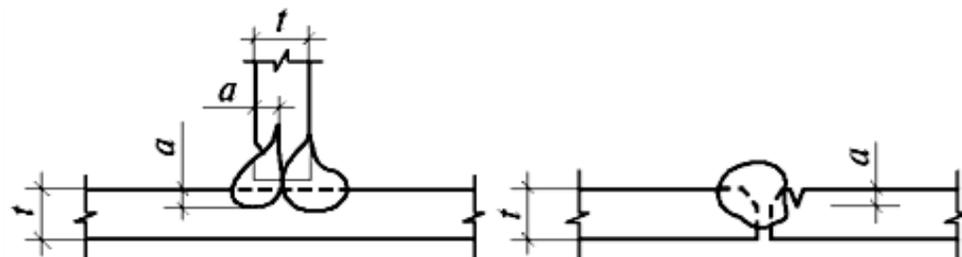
Подрезы основного металла угловых и стыковых соединений
